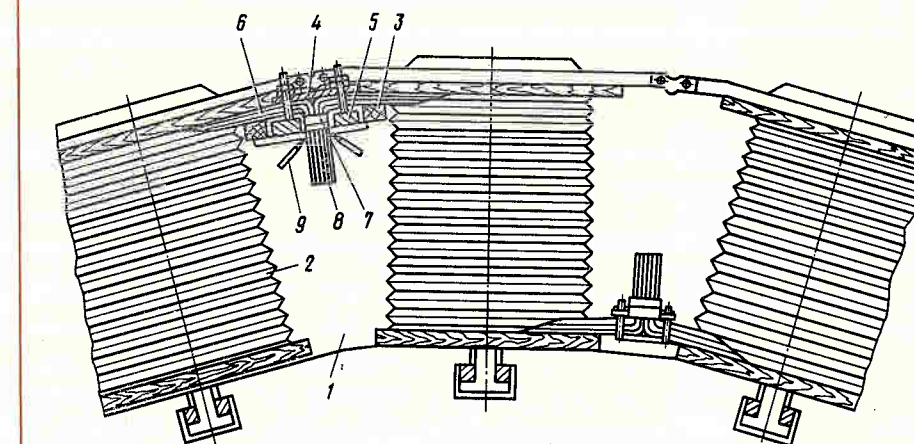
Обрубка концов и подготовка к пайке междуполусных соединений:
